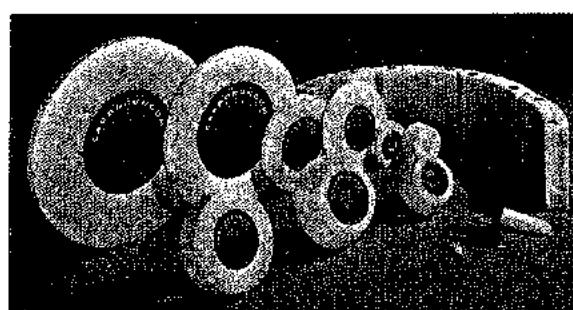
Diversidad de muelas, segmentos y puntos montados para el taller de utilaje (The Carborundum Co.)
